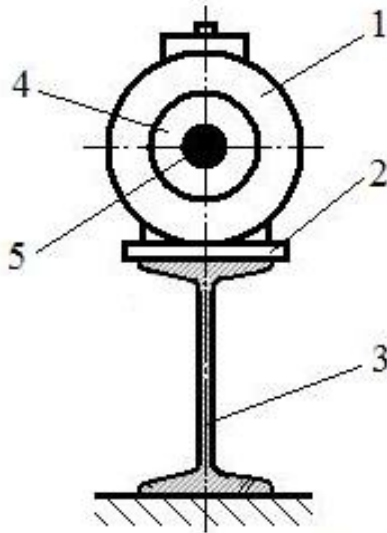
Загальний вигляд електродвигуна привода конвертора: 1 – двигун; 2 – платформа; 3 – стояк; 4 – ротор; 5 – вал
